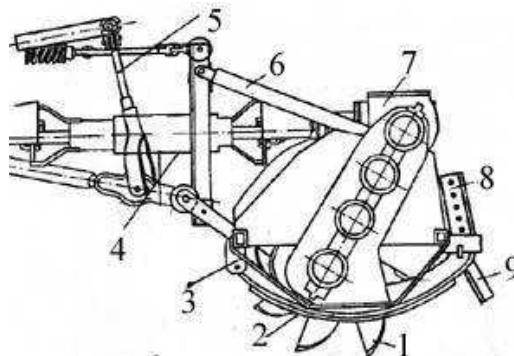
Фреза ФЛУ-0,8: 1 – ведомый диск с ножами; 2 – опорная лыжа; 3 – рама; 4 – карданный привод; 5 – навесная система трактора; 6 – навеска фрезы; 7 – редуктор; 8 – регулировочный кронштейн; 9 – гребенка
